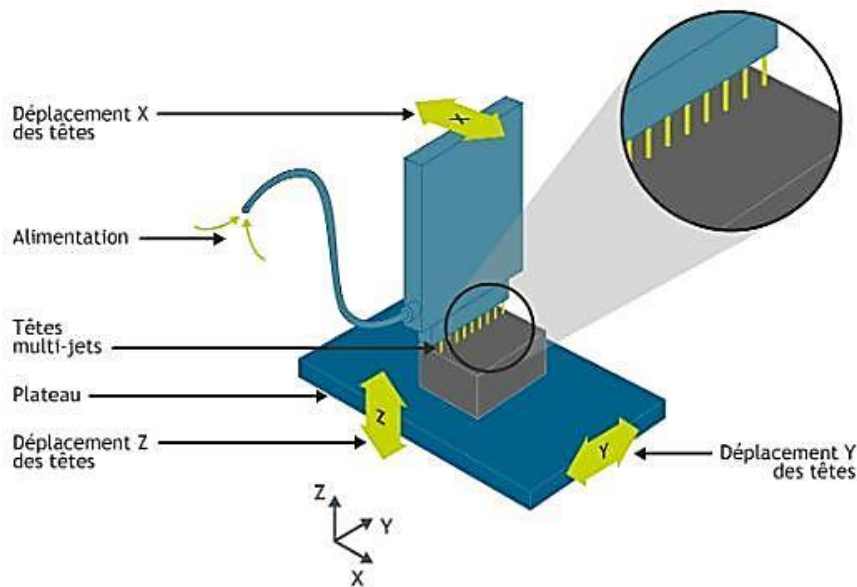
Principe de fabrication par projection de gouttes.[6]
